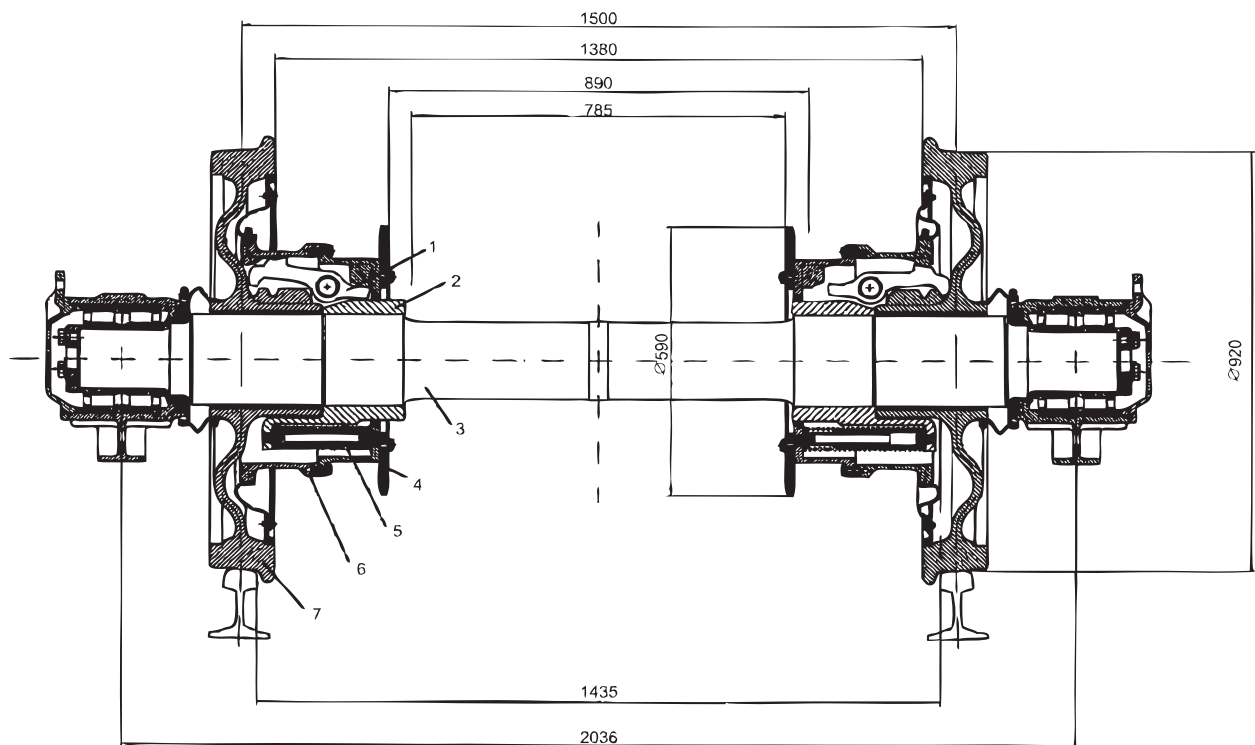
Раздвижная колесная пара системы DB AG/Rafil Type V: 1 — механизм блокирования; 2 — пружинистая втулка; 3 — ось; 4 — размыкающий диск; 5 — пружина сжатия; 6 — фланец механизма блокирования; 7 — колесо
